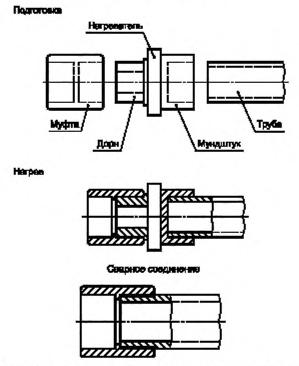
Принцип сварки нагретым инструментом в раструб
